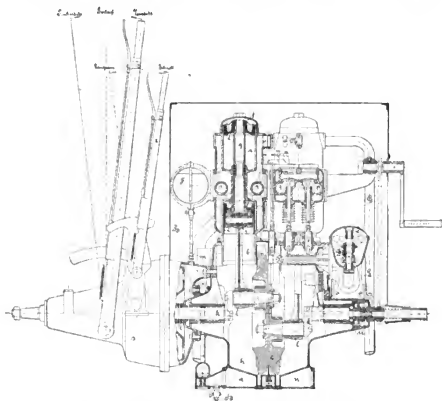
Vierzylinder-Motor mit Doppelkolben, Wolf & Struck.
